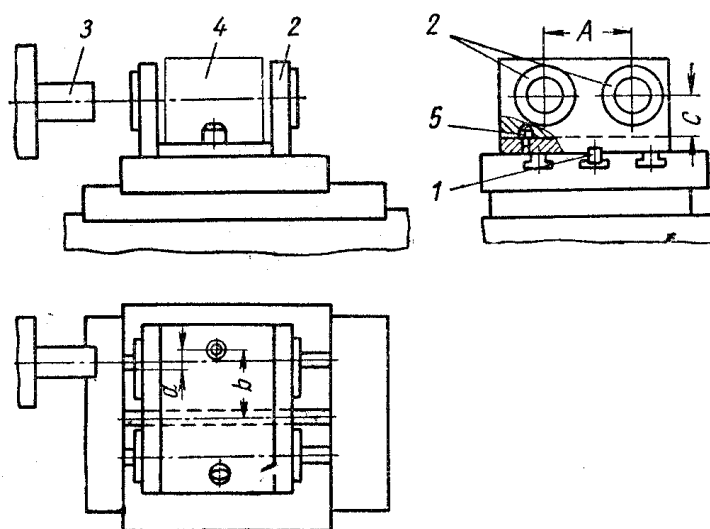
Схема установлення корпусної деталі в кондукторі
